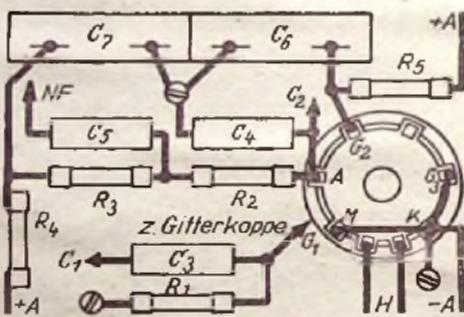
Verdrahtungsplan einer Audionstufe für Pentoden mit Außenkontaktschaltung
